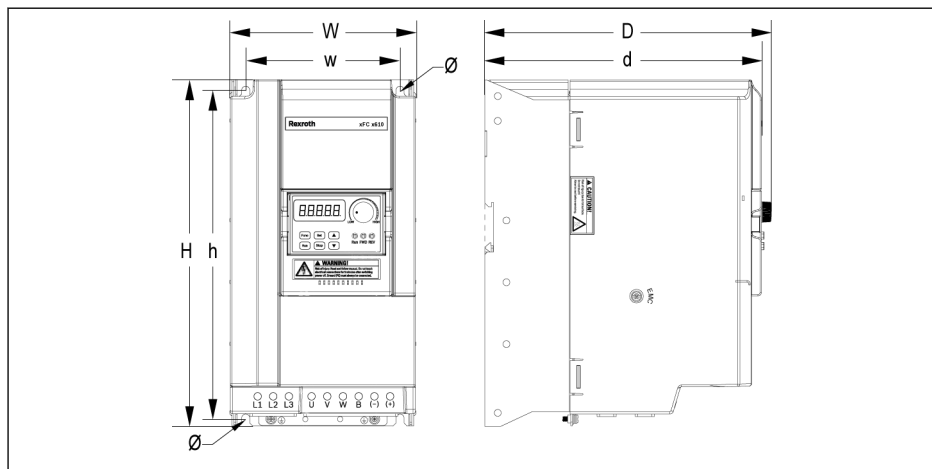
Размерный чертеж VFC x610 5K50...18K5
